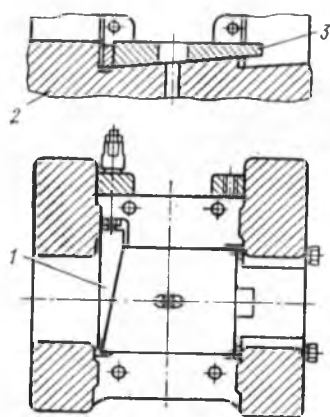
Клиновое устройство для регулирования закрытой высоты КГШП
